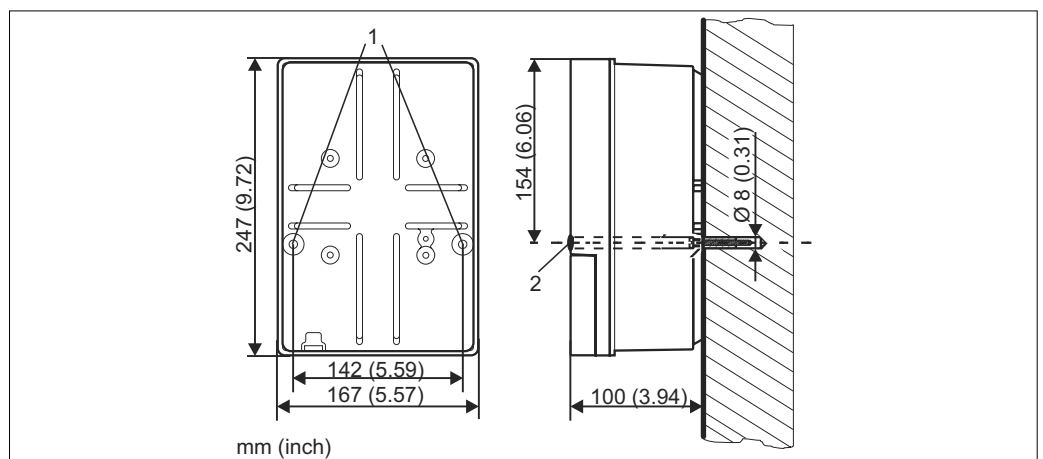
Dimensions pour le montage mural, vis de fixation : Ø 6 mm (0,24"), cheville : Ø 8 mm (0,31")
